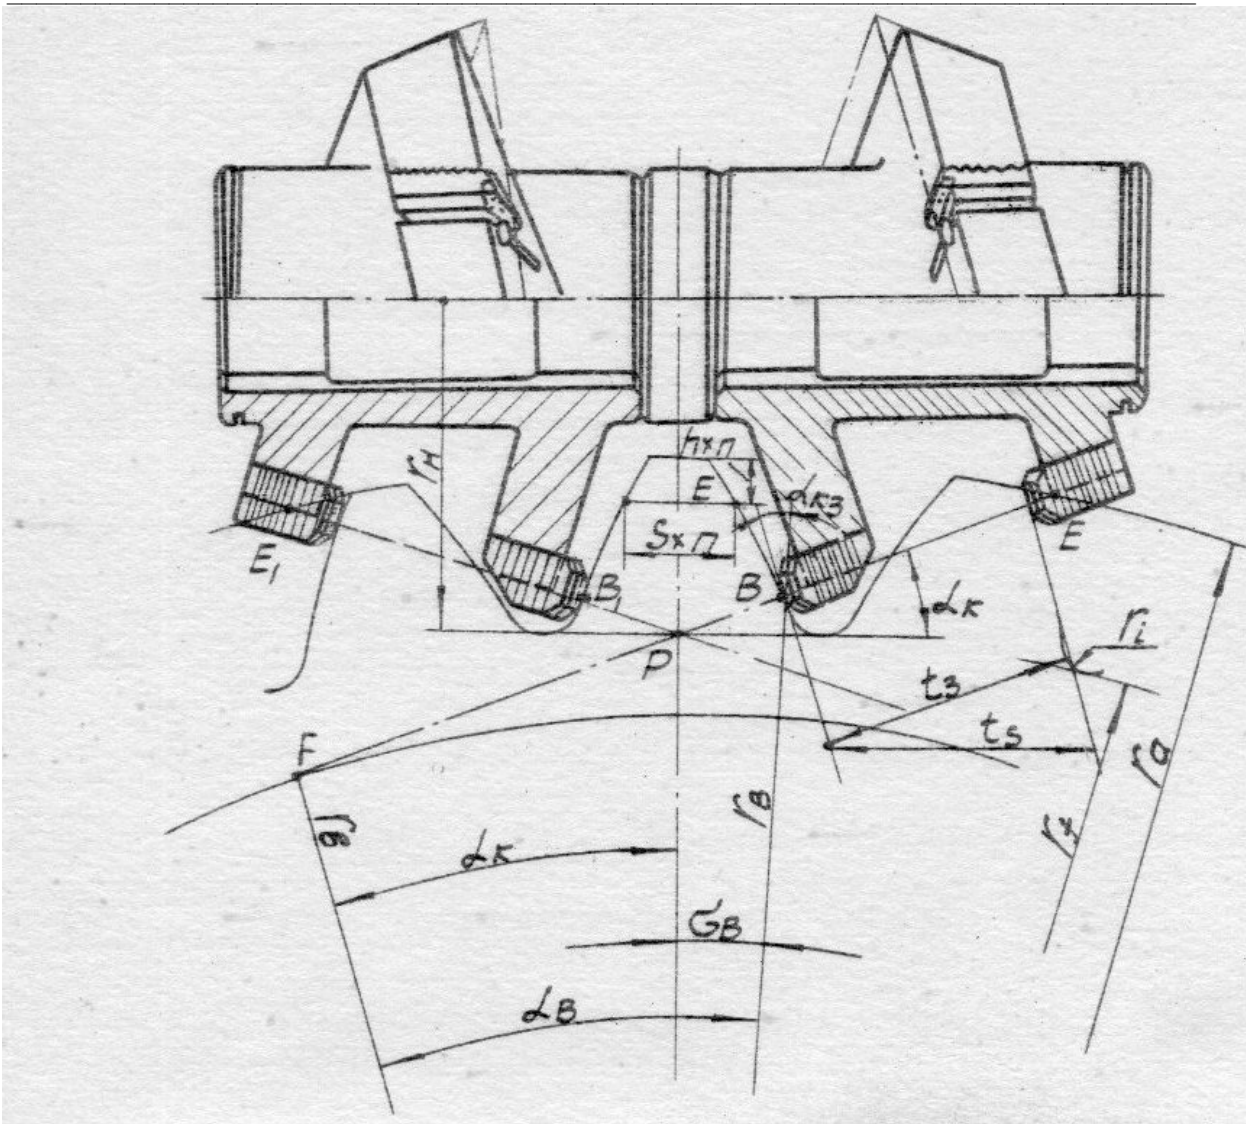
Схема станочного зацеплення спеціальної твердосплавної фрези з оброблюваним колесом.
